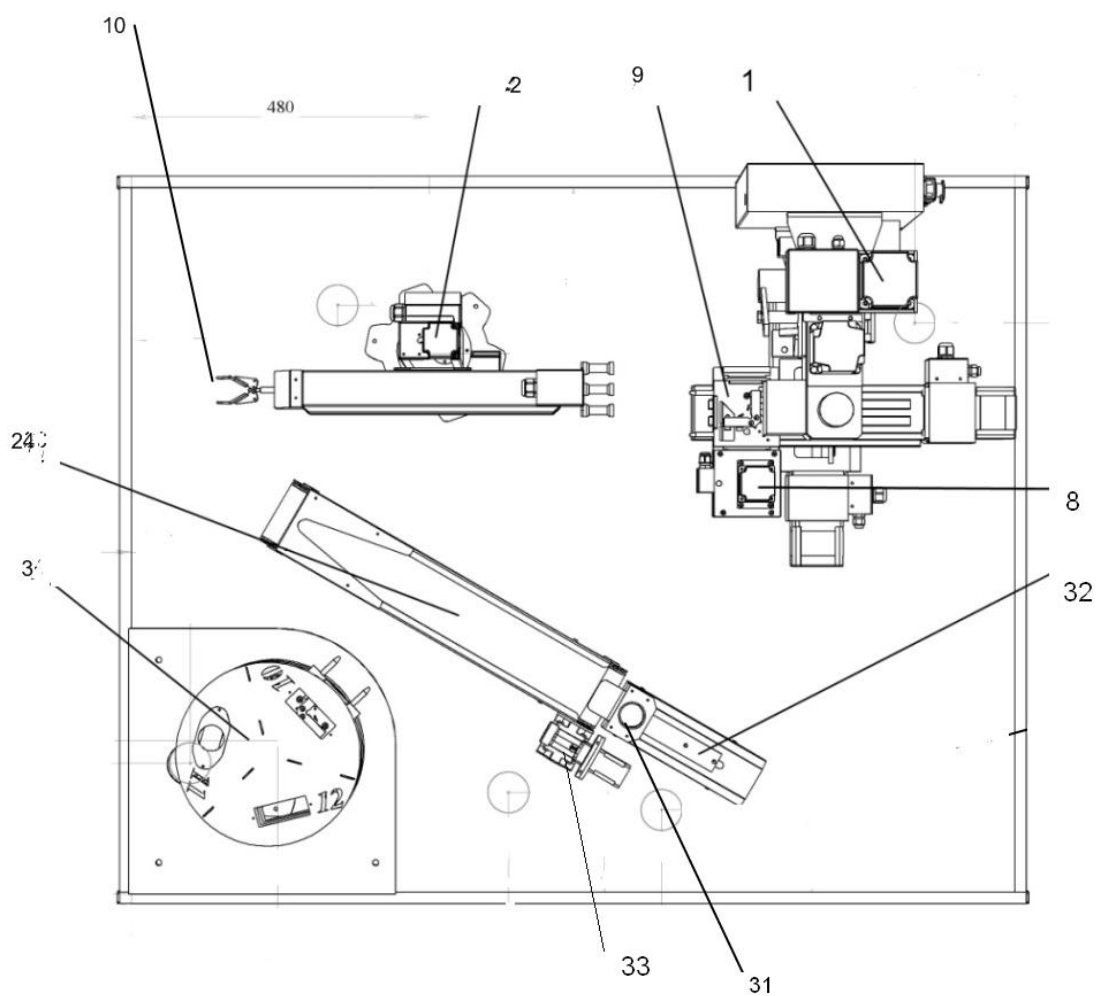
Компонировка модели ГПП на базе многоцелевого станка, поворотного стеллажа с приспособлениями-спутниками
